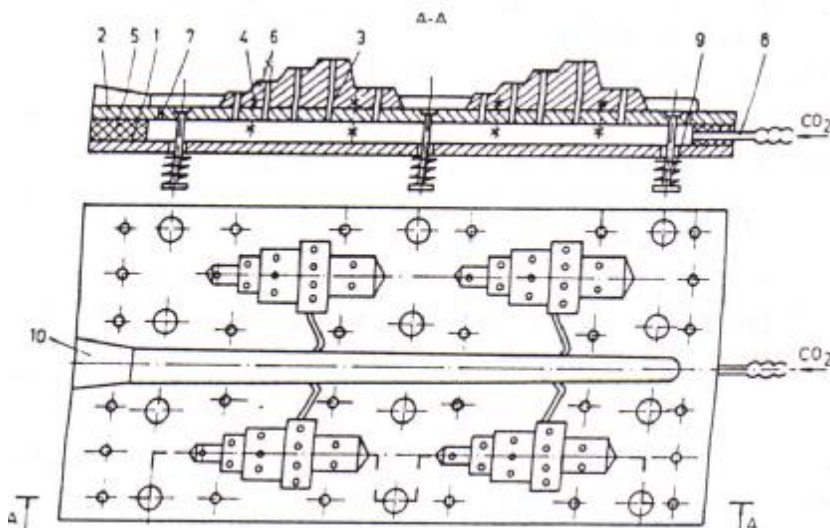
Placă portmodel pentru executarea formelor coji din amestec pe bază de silicat de sodiu și întărire chimică cu CO₂: 1-placă inferioară; 2-placă superioară; 3-modele metalice; 4-șuruburi de fixare; 5-garnitură de cauciuc; 6-orificiu de insuflare prin model; 7-orificiu de insuflare prin placă; 8-conductă de alimentare cu CO₂; 9-extractoare; 10-modelul rețelei de turnare.
